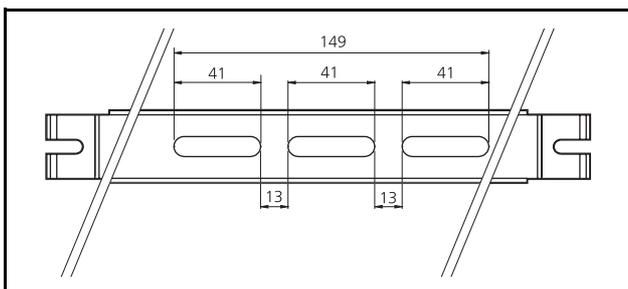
Disposition des trous, fixation au plafond MD10S, Vue de dessus.
